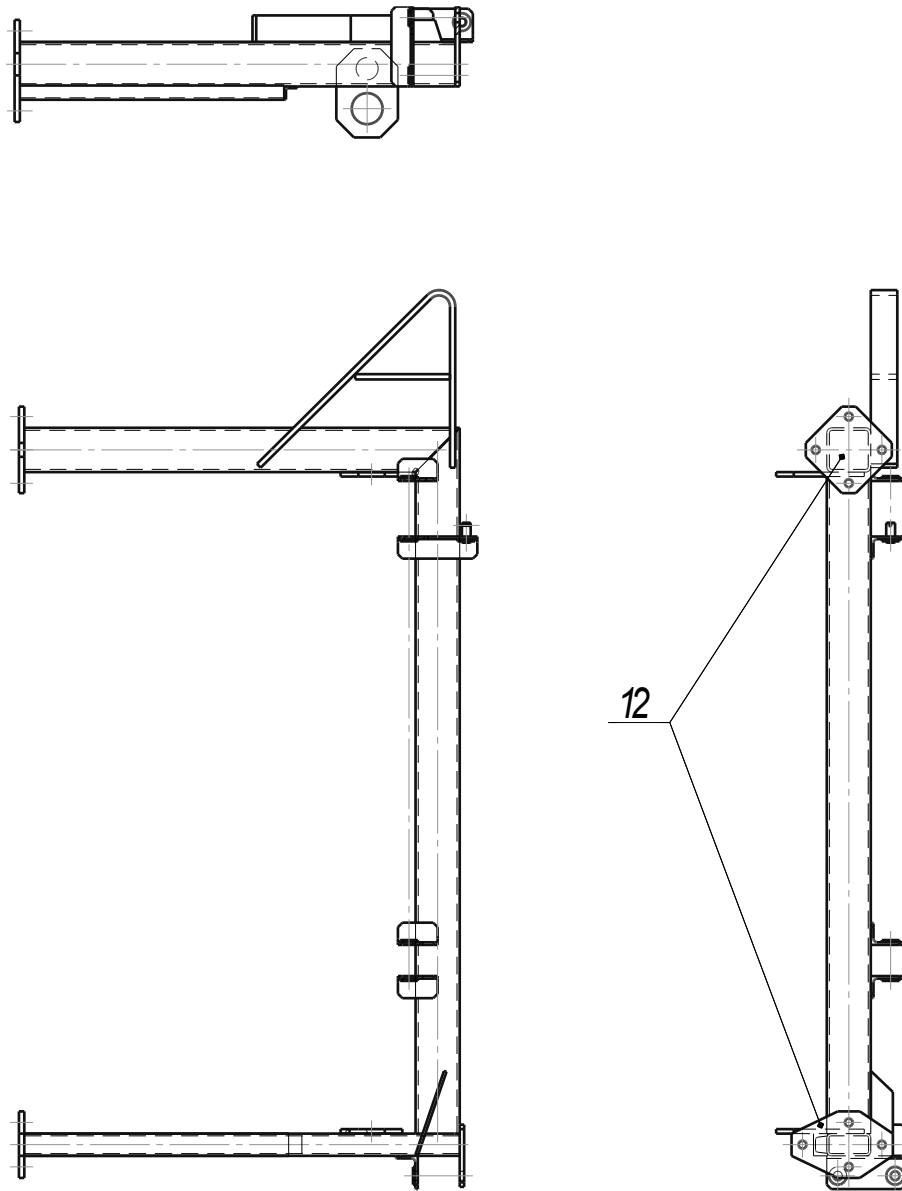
Рама бокова культиватора КП-8,5
